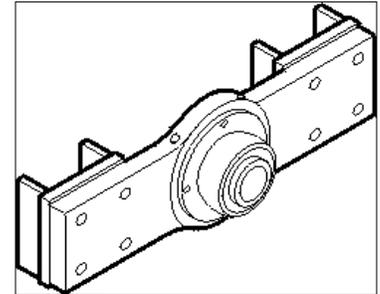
MONTAJE RODAMIENTO ESFÉRICO DE UN ÚNICO BRAZO
